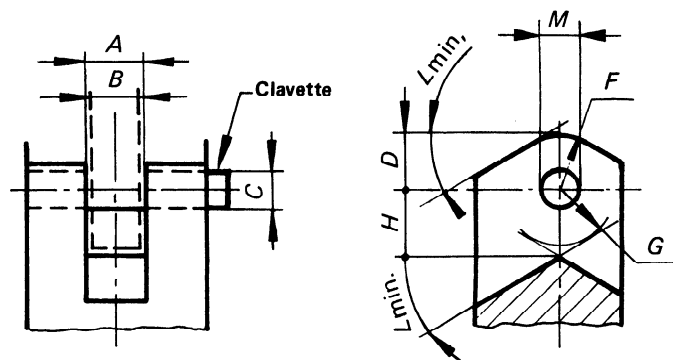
Chape d'extrémité mobile — Schéma d'encombrement
